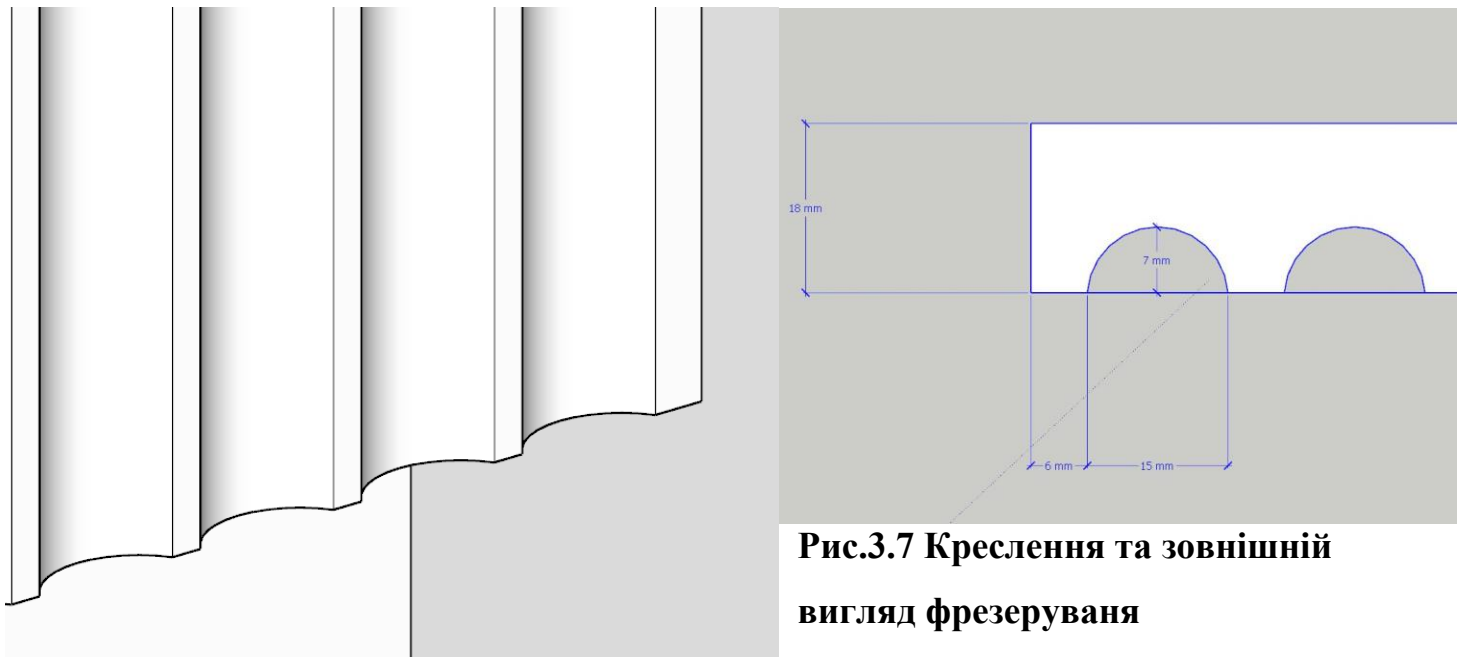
Креслення та зовнішній вигляд фрезерування
